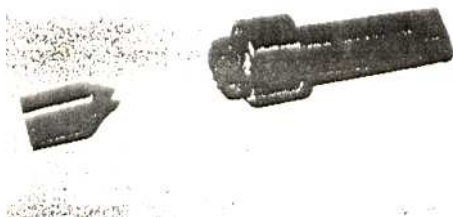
Вид разрушения паяного металлокерамического образца при кручении
